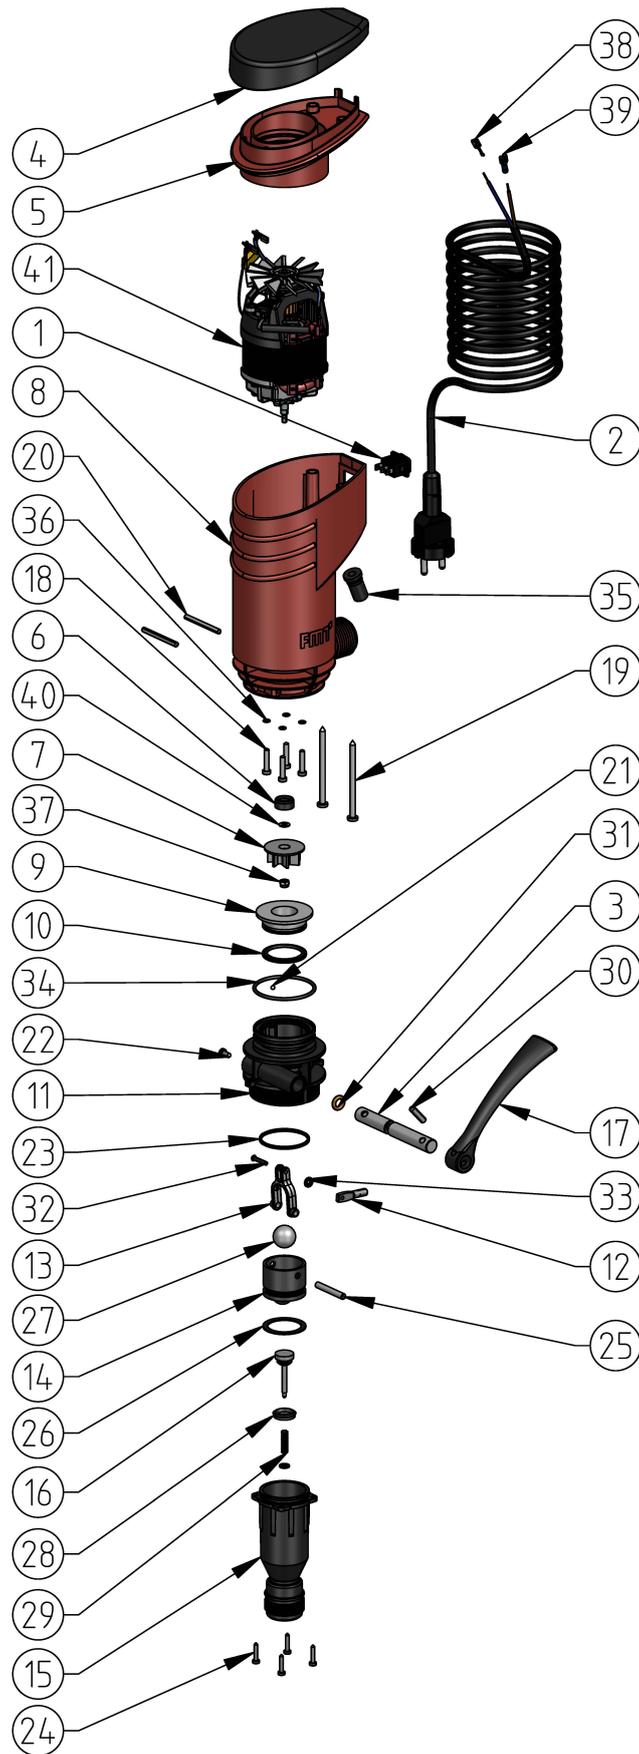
1: Vue éclatée de la pompe diesel PREMAxx 230 V
